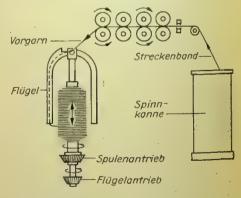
Flyer mit Walzenstreckwerk (Schema)
